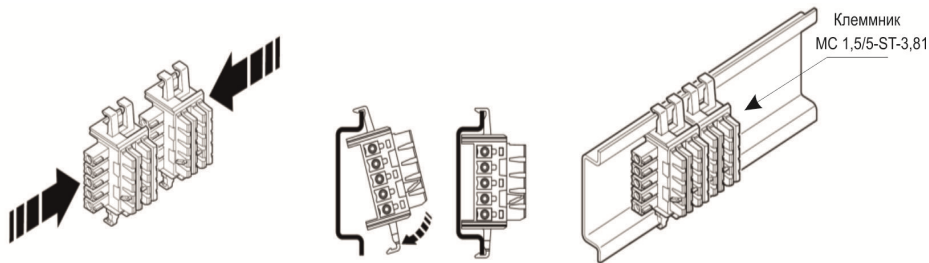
Установка шинных соединителей на DIN- рейку
